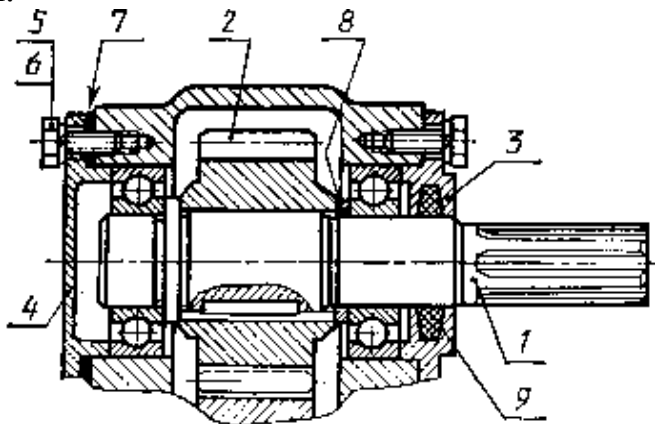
Нанесение номеров позиций на сборочных чертежах
